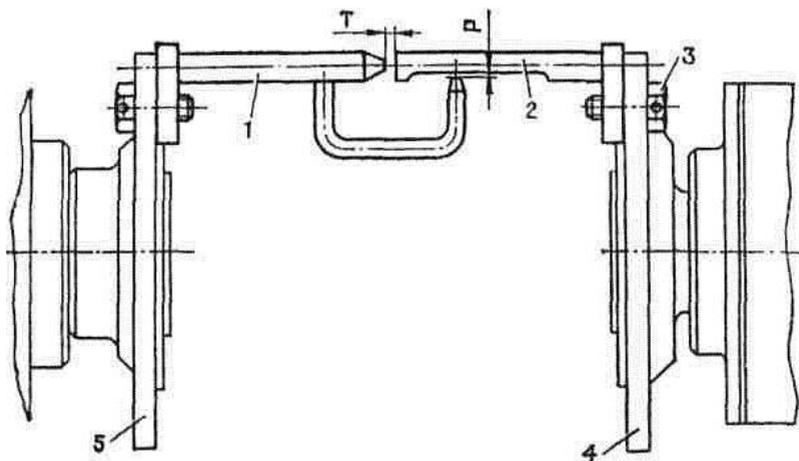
Установка приспособления 175.95.063С6 для центровки привода гитары со стартером-генератором танка Т-72:
